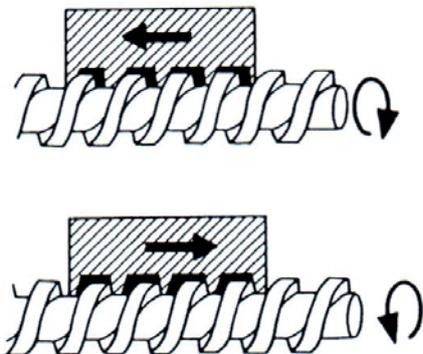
Spiel bei Gewindespindeln bei handbedienten Maschinen
